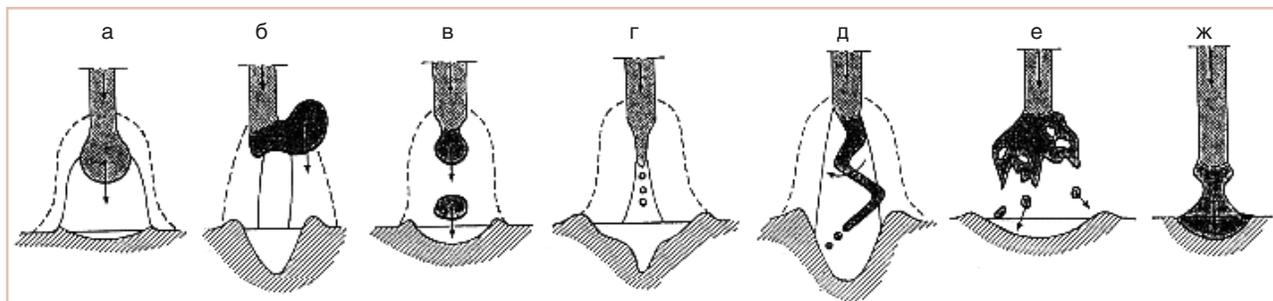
Влияние типа переноса электродного металла на форму проплавления по классификации Международного института сварки: а — капельный; б — крупнокапельный; в — мелкокапельный; г — струйный; д — струйно-вращательный; е — со взрывом капли (проволока неудовлетворительного качества); ж — с короткими замыканиями
